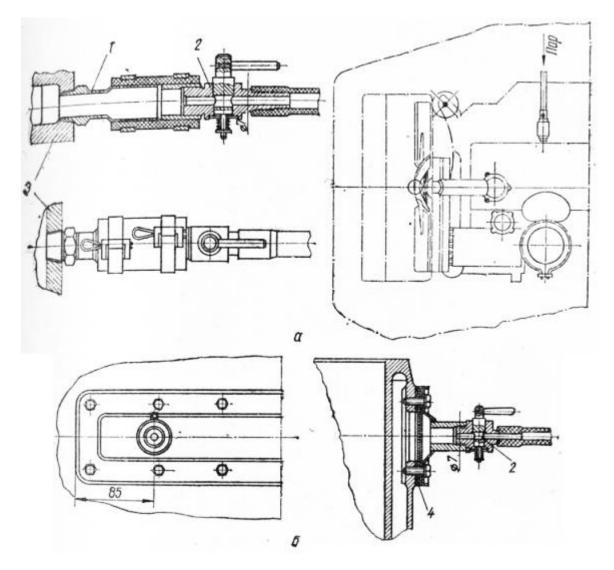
Аппаратура для ввода пара в систему охлаждения при разогреве двигателей: а — ГАЗ-51; б —ЗИЛ-120; 1 — штуцер; 2 —кран; 3 — головка блока; 4 — распределительная пластинка
